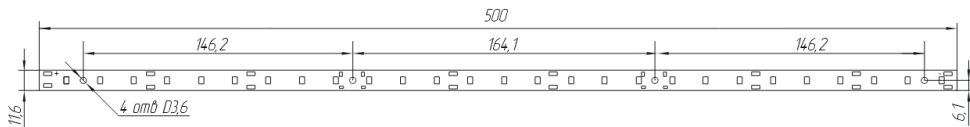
Внешний вид с габаритными и присоединительными размерами СДПП LUXE
